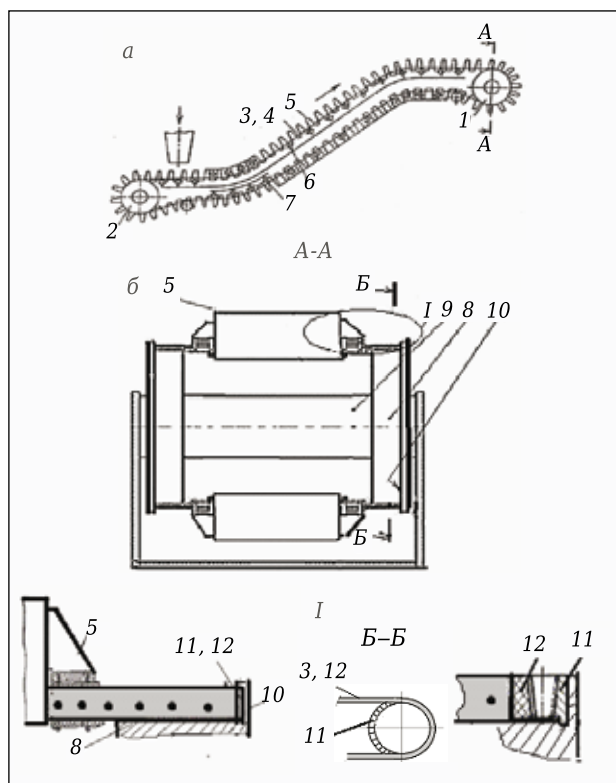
Ковшовый ленточный конвейер: а — общий вид; б — взаимодействие зубчатых кольцевых дисков с гибкими зубчатыми ремнями
